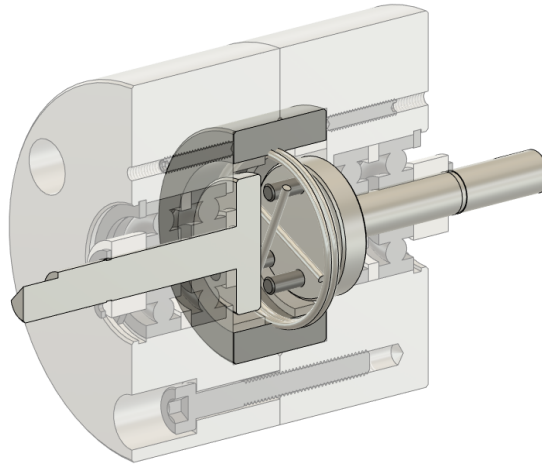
Vue de coupe du prototype de NBDM (CAO)
